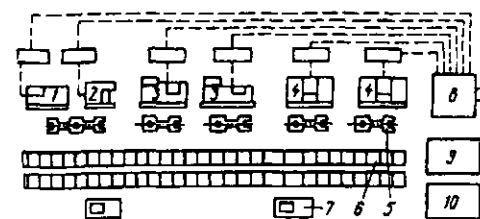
Гибкая производственная система для обработки деталей типа тел вращения со станками с ручным управлением и с ЧПУ: 1 – протяжной станок; 2 – зубофрезерный станок; 3, 4 – токарные станки с ЧПУ; 5 – промышленные роботы для загрузки-разгрузки станков; 6 – конвейер-накопитель; 7 – позиции загрузки заготовок; 8 – центральная ЭВМ; 9 – ЭВМ управления транспортом; 10 – ЭВМ управления контролем и наладкой инструмента
